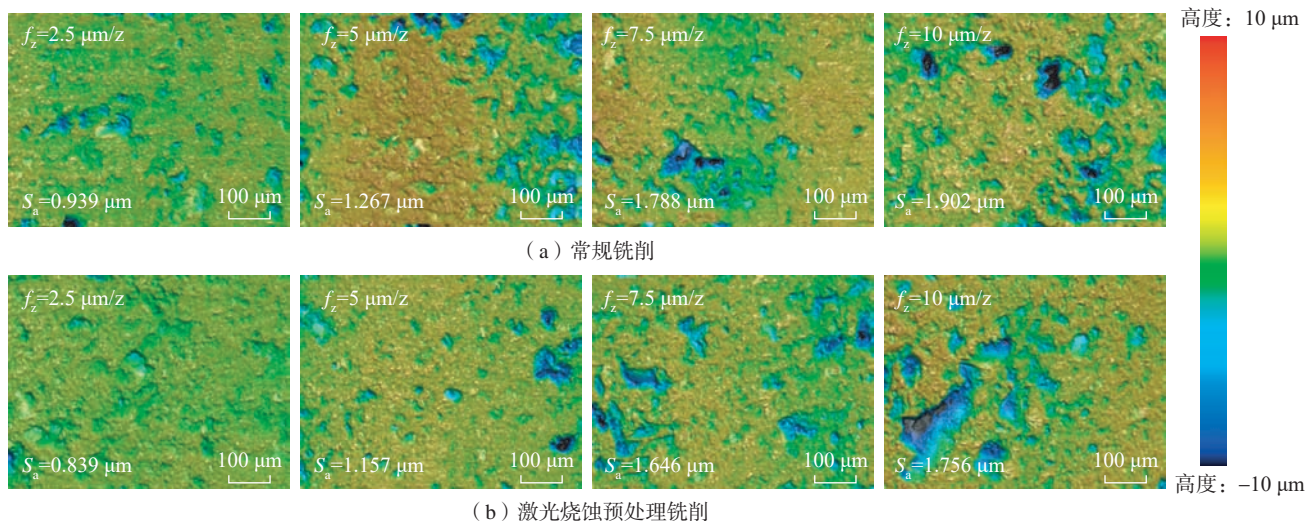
常规铣削和激光烧蚀预处理铣削加工表面三维形貌
